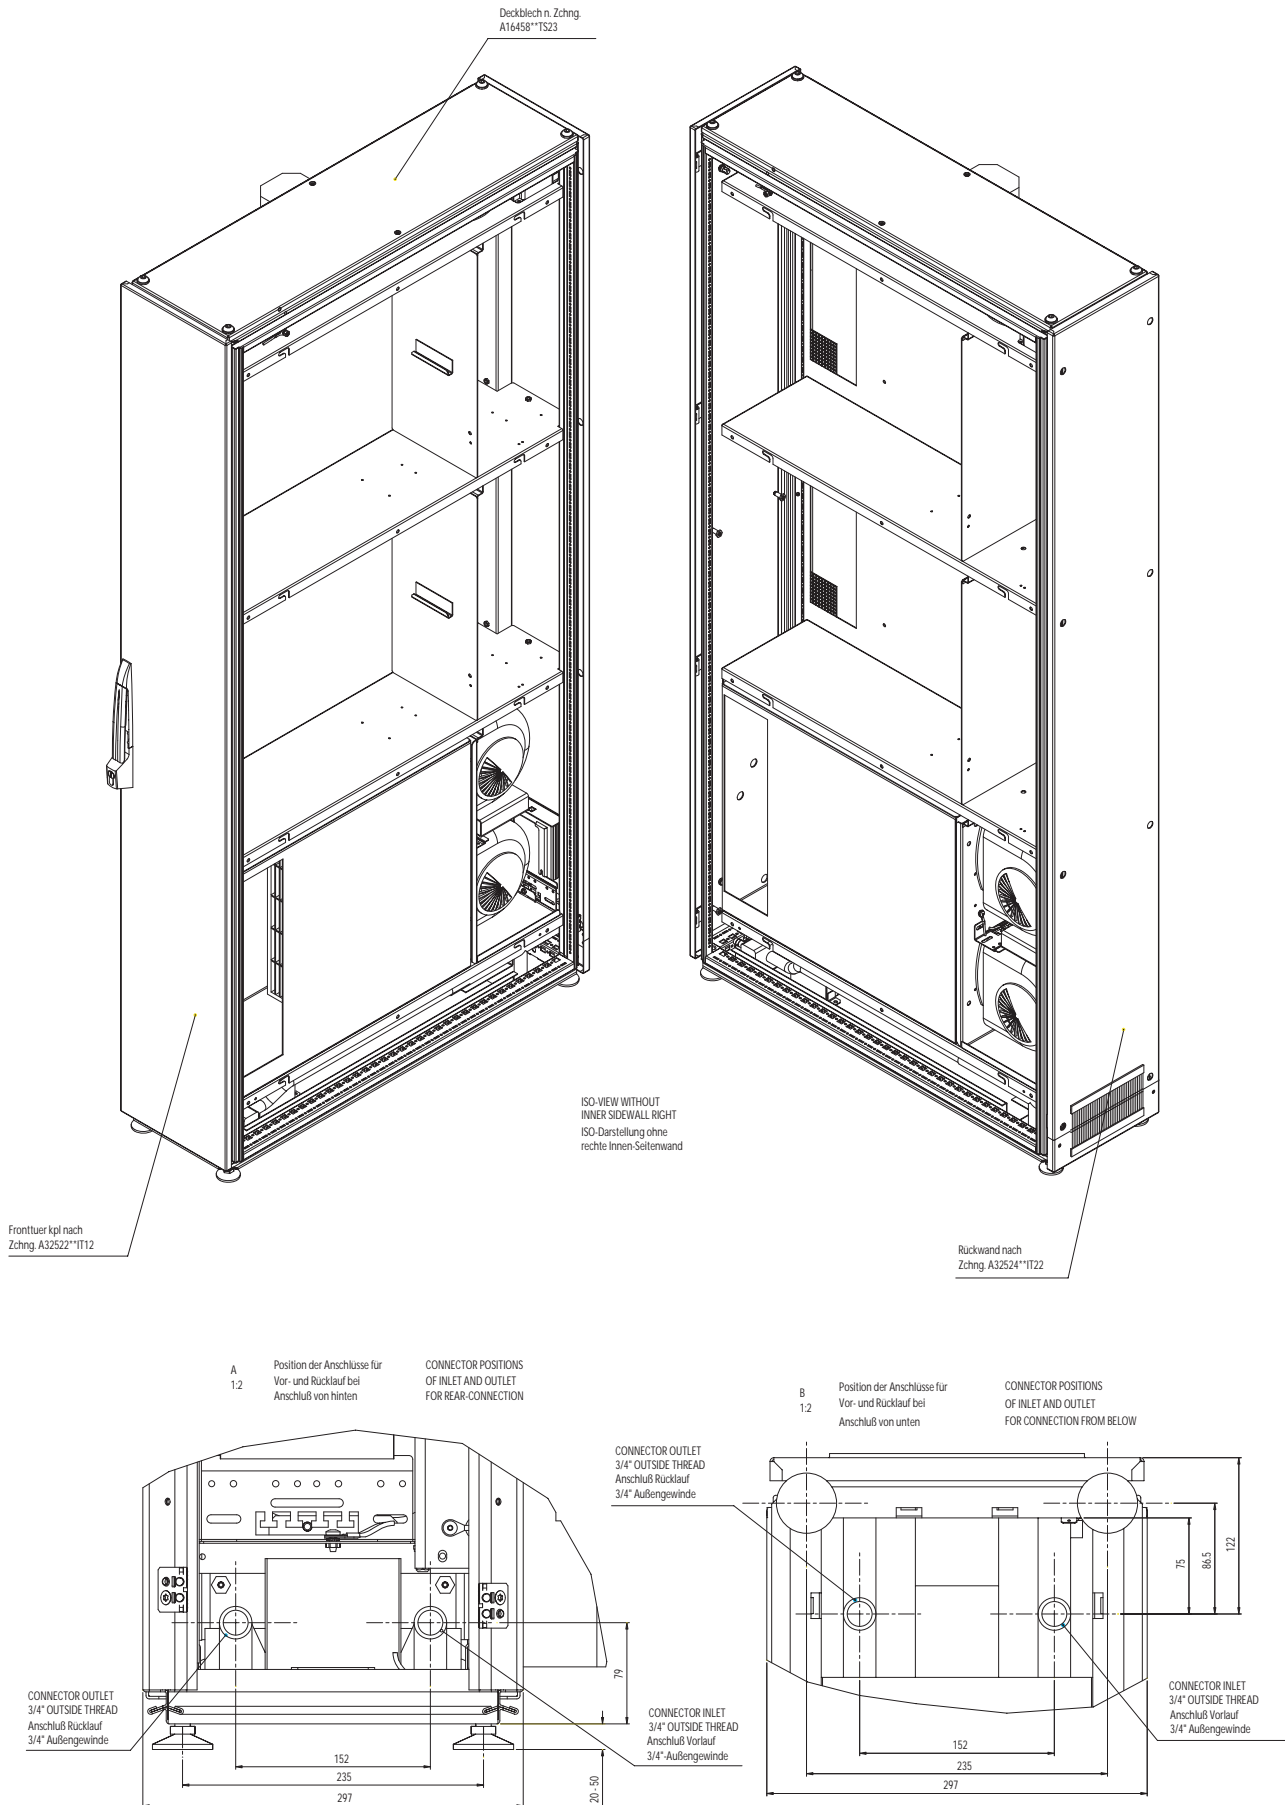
Übersichtszeichnung - Liquid Cooling Package (Isometrie, Detail A und Detail B)
